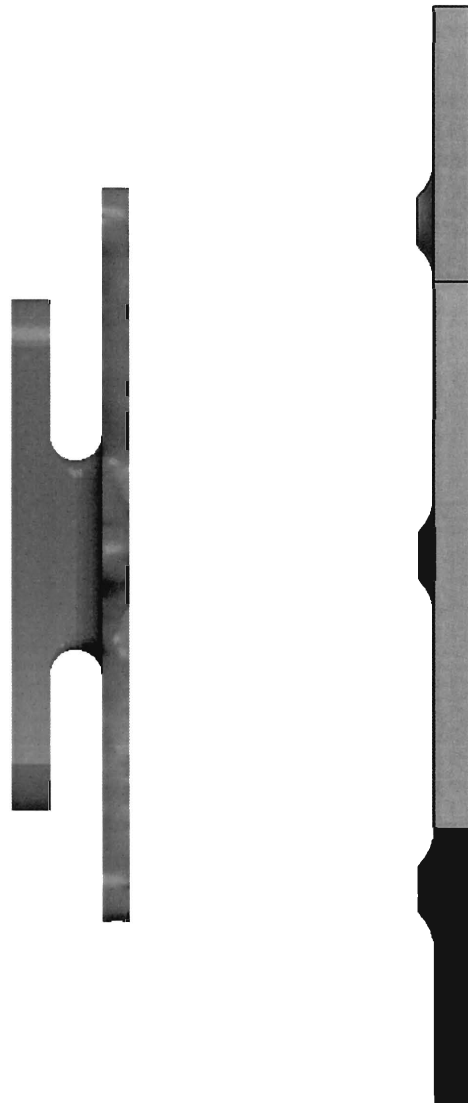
Vedere laterală explodată ansamblu – TIP 1
